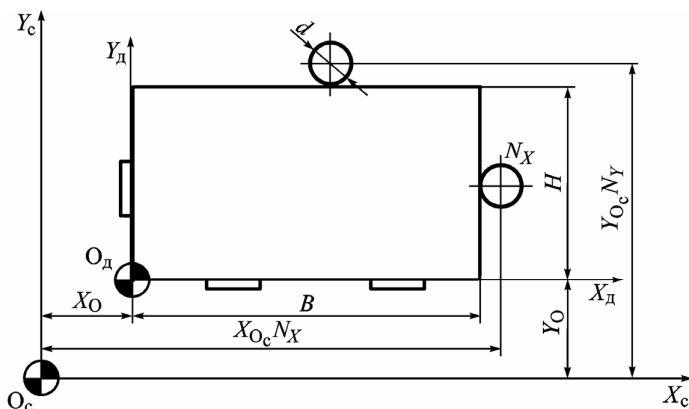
Схема установки приспособления на столе станка без строгой фиксации положения относительно базовой точки
